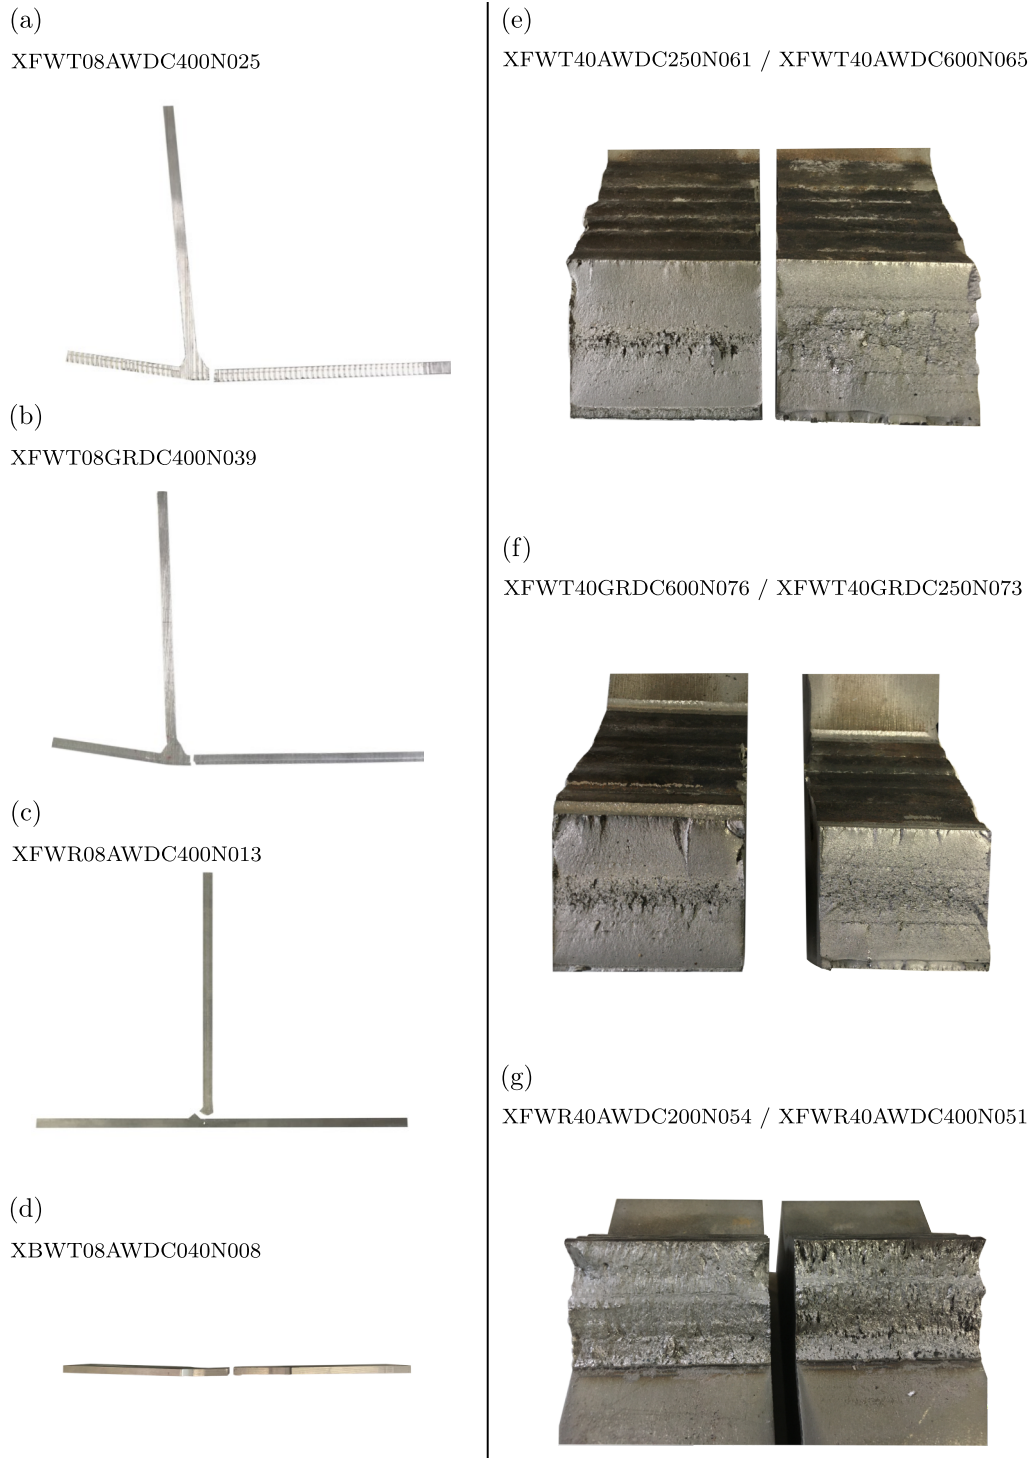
Schweißverbindungsproben aus 1.4541 nach Versuchsende. (a)-(d) Seitenansicht der Proben mit 8 mm Blechdicke. (e)-(g) Draufsicht auf die Bruchflächen der gebrochenen Proben mit 40 mm Blechdicke bei jeweils unterschiedlichen Lastniveaus (mit Änderungen entnommen aus [67]).
